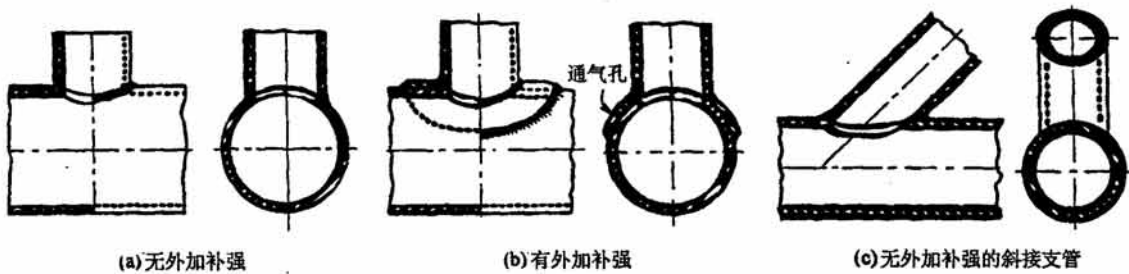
A、B、C 典型的焊接支管连接件
